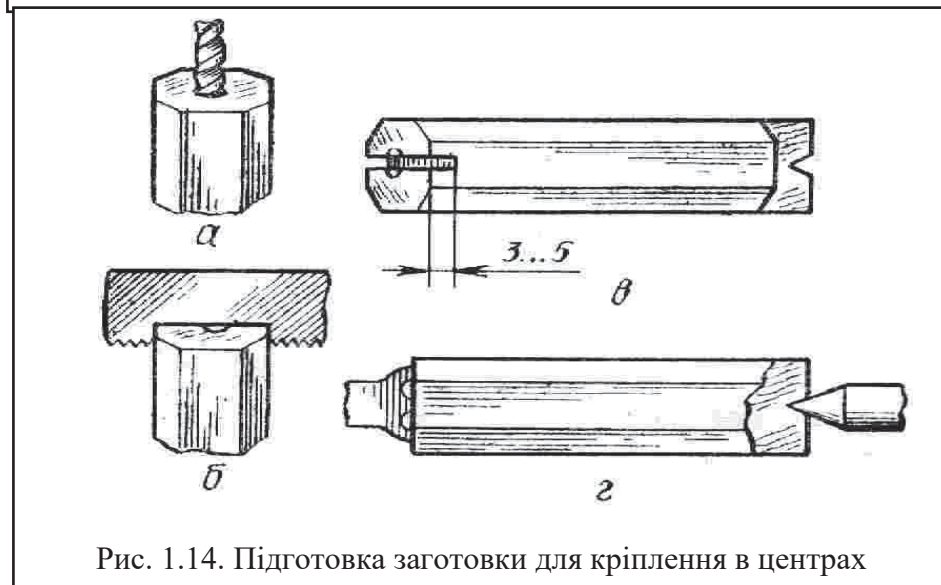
Підготовка заготовки для кріплення в центрах
